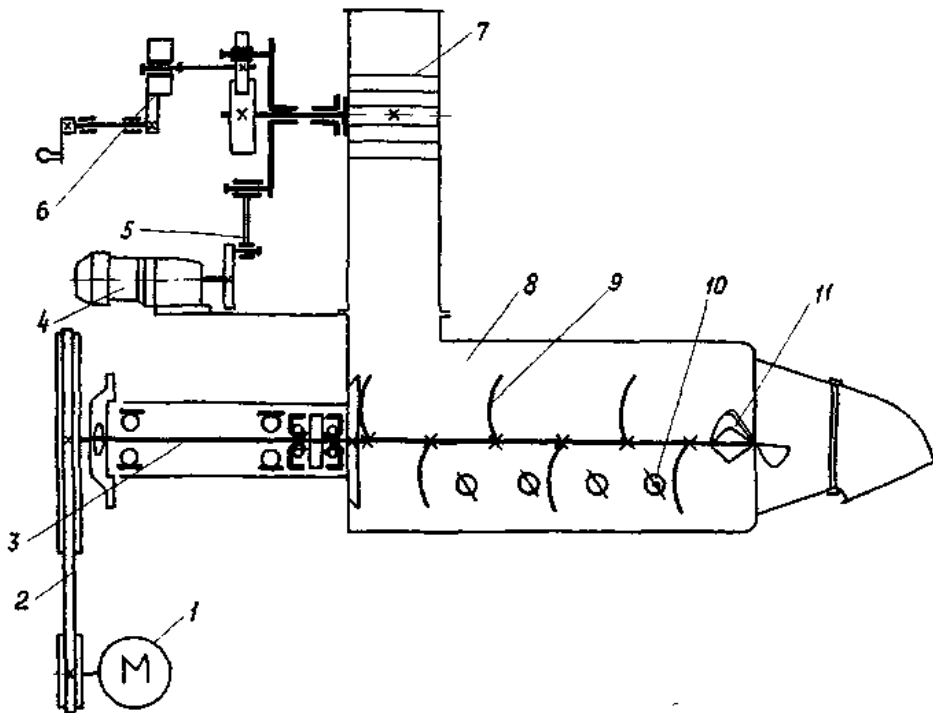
Схема тістомісильної машини безперервної дії: 1 — електродвигун; 2 — клинопасова передача; 3 — місильний вал з лопастями; 4 — редуктор, 5 — шатун, 6 — механізм регулювання продуктивності, 7 — роторний дозатор борошна, 8 — місильна камера, 9 — лопать; 10 — гальмівна лопать, 11 — пластифікатор
